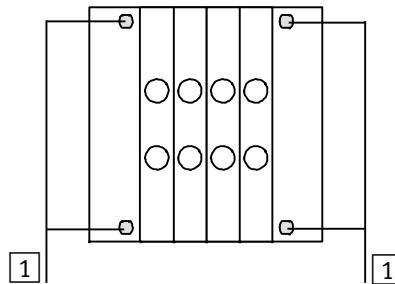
/4: Befestigungsbohrungen für die Fußmontage
